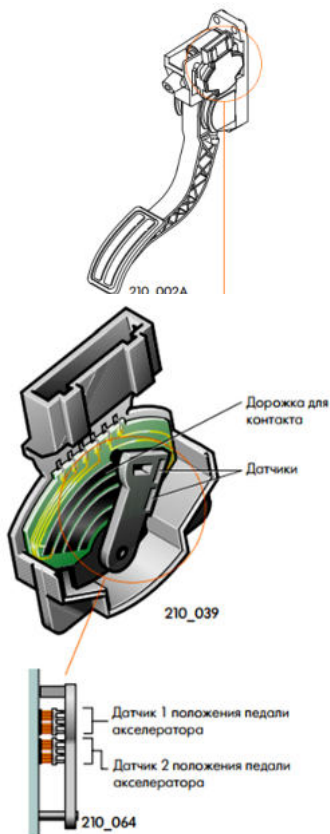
Разрез корпуса модуля педали акселератора с датчиками G79 и G185
